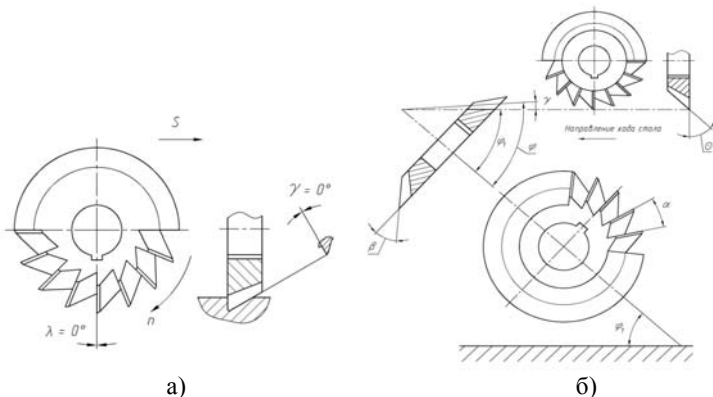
Угловая фреза с нулевой геометрией а) – общая схема, б) - схема фрезерования стружечных канавок угловой фрезы с нулевой геометрией)
